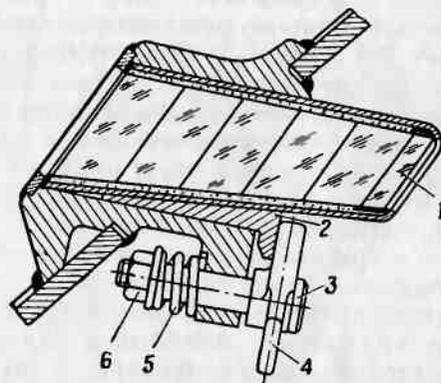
Крепление прибора наблюдения в крышке люка лобового листа:
